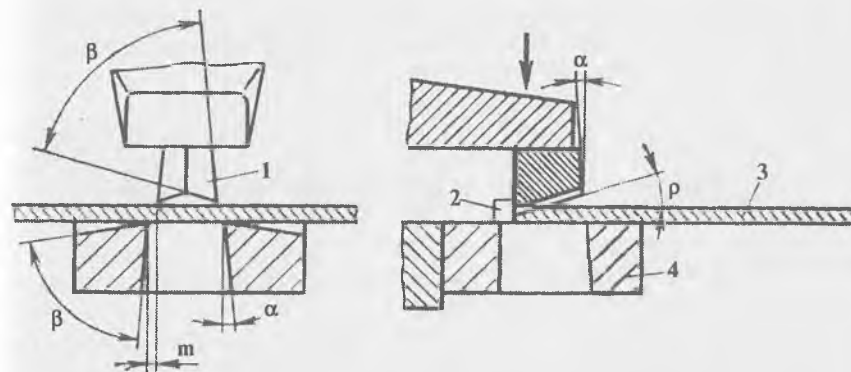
Схема приспособления для нарезания зубьев ручных пил:
